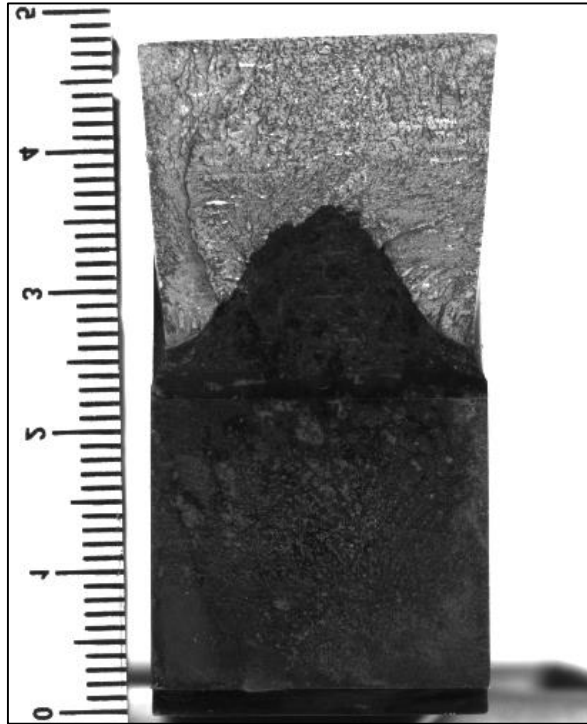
Fractografia da superfície de fratura do corpo de prova SE(B) do metal de solda de aço API X65 com recobrimento.
